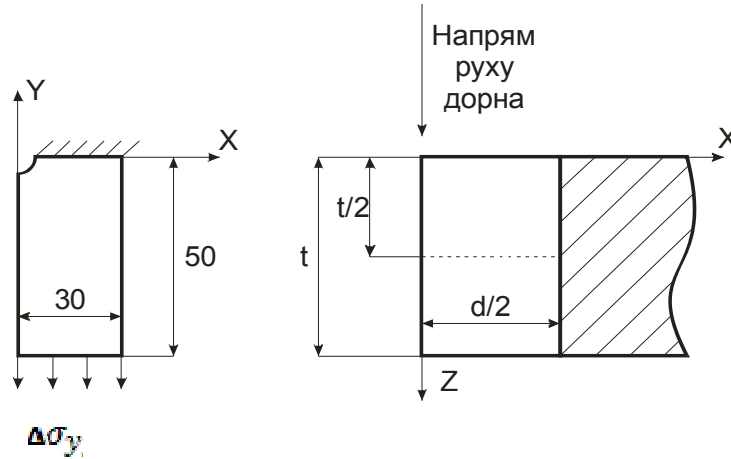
Схематичне креслення чверті робочої ділянки зразка.
